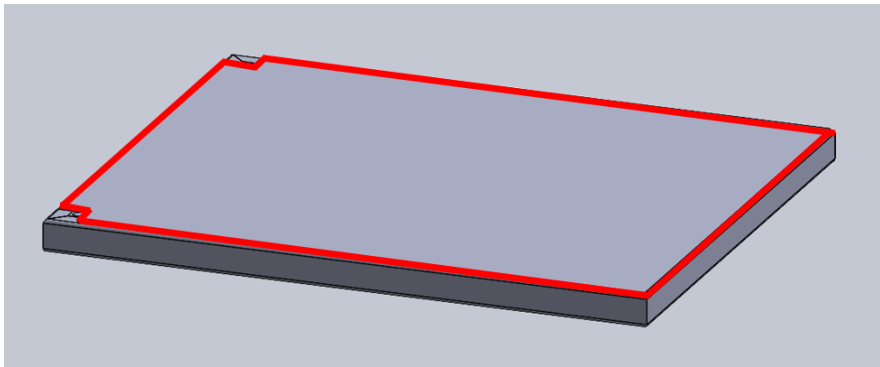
Superficie del cordón de soldadura TIG para la unión CHAPA-CHASIS [fuente propia]
